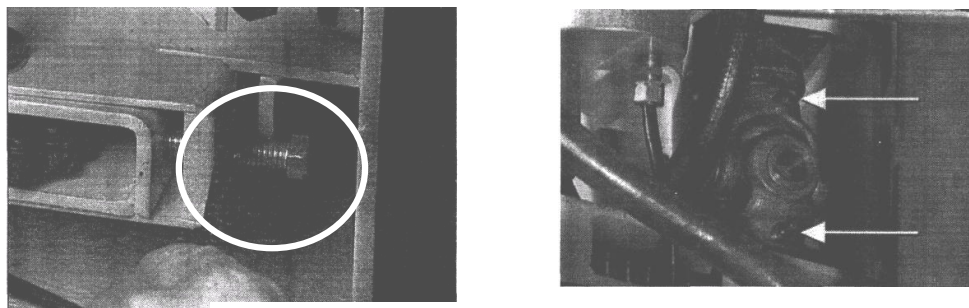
ENSAMBLAJES DE DIRECCIÓN
